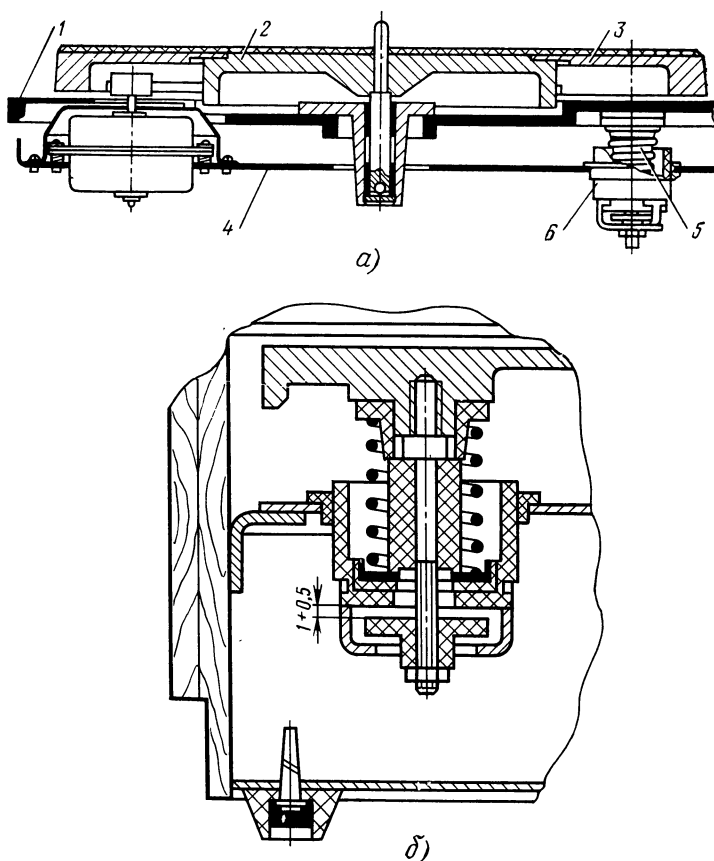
Схемы крепления плиты проигрывателя (а) и амортизатора (б): 1 — плита; 2 — малый диск; 3 — большой диск; 4 — шасси; 5 — пружины; 6 — стаканы для крепления пружин
